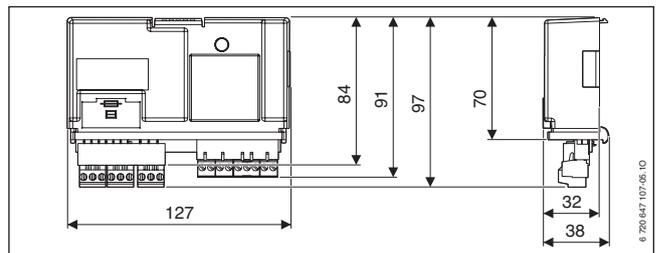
Abmessungen Solarmodul SM50 bei Einbau in den Wärmeezeuger (Maße in mm)
